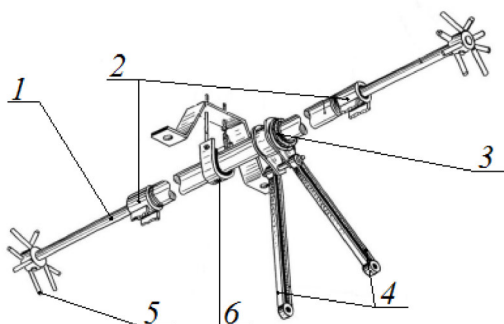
Рыхлитель (сводоразрушитель): 1 – вал; 2 – опора; 3 – муфта обгонная; 4 – тяги; 5 – рыхлитель (сводоразрушитель); 6 – тормоз
